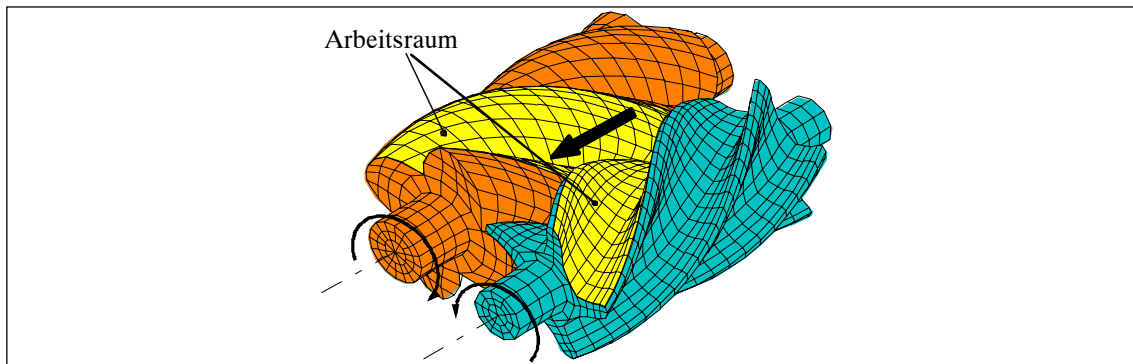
Arbeitsspiel des Schraubenkompressors – Kompression
